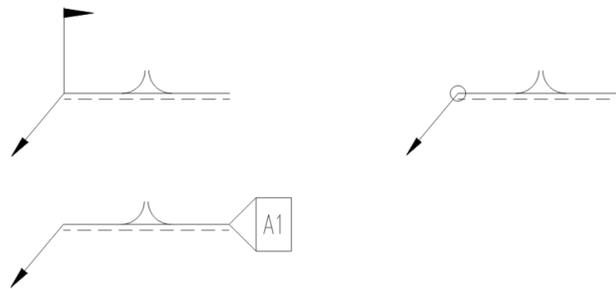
Schweißsymbol (Baustellennaht, Ringsumnaht, Bezugsnaht)
